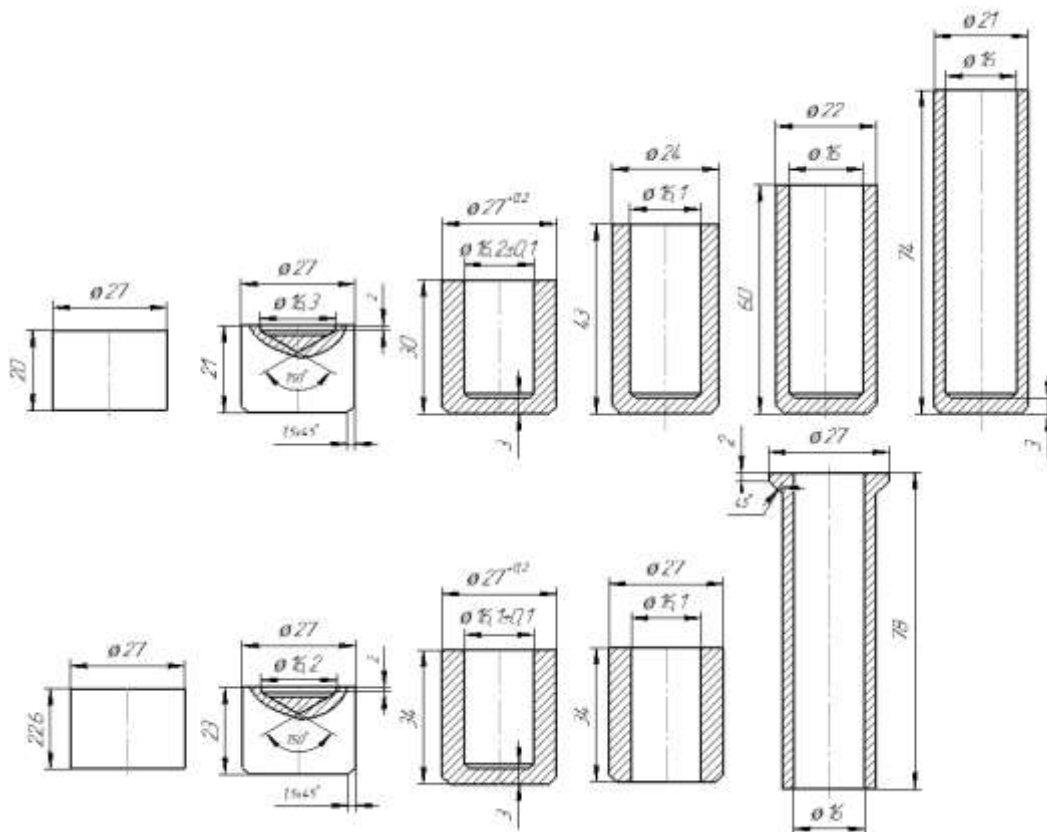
Послідовність виготовлення порожнистих деталей
